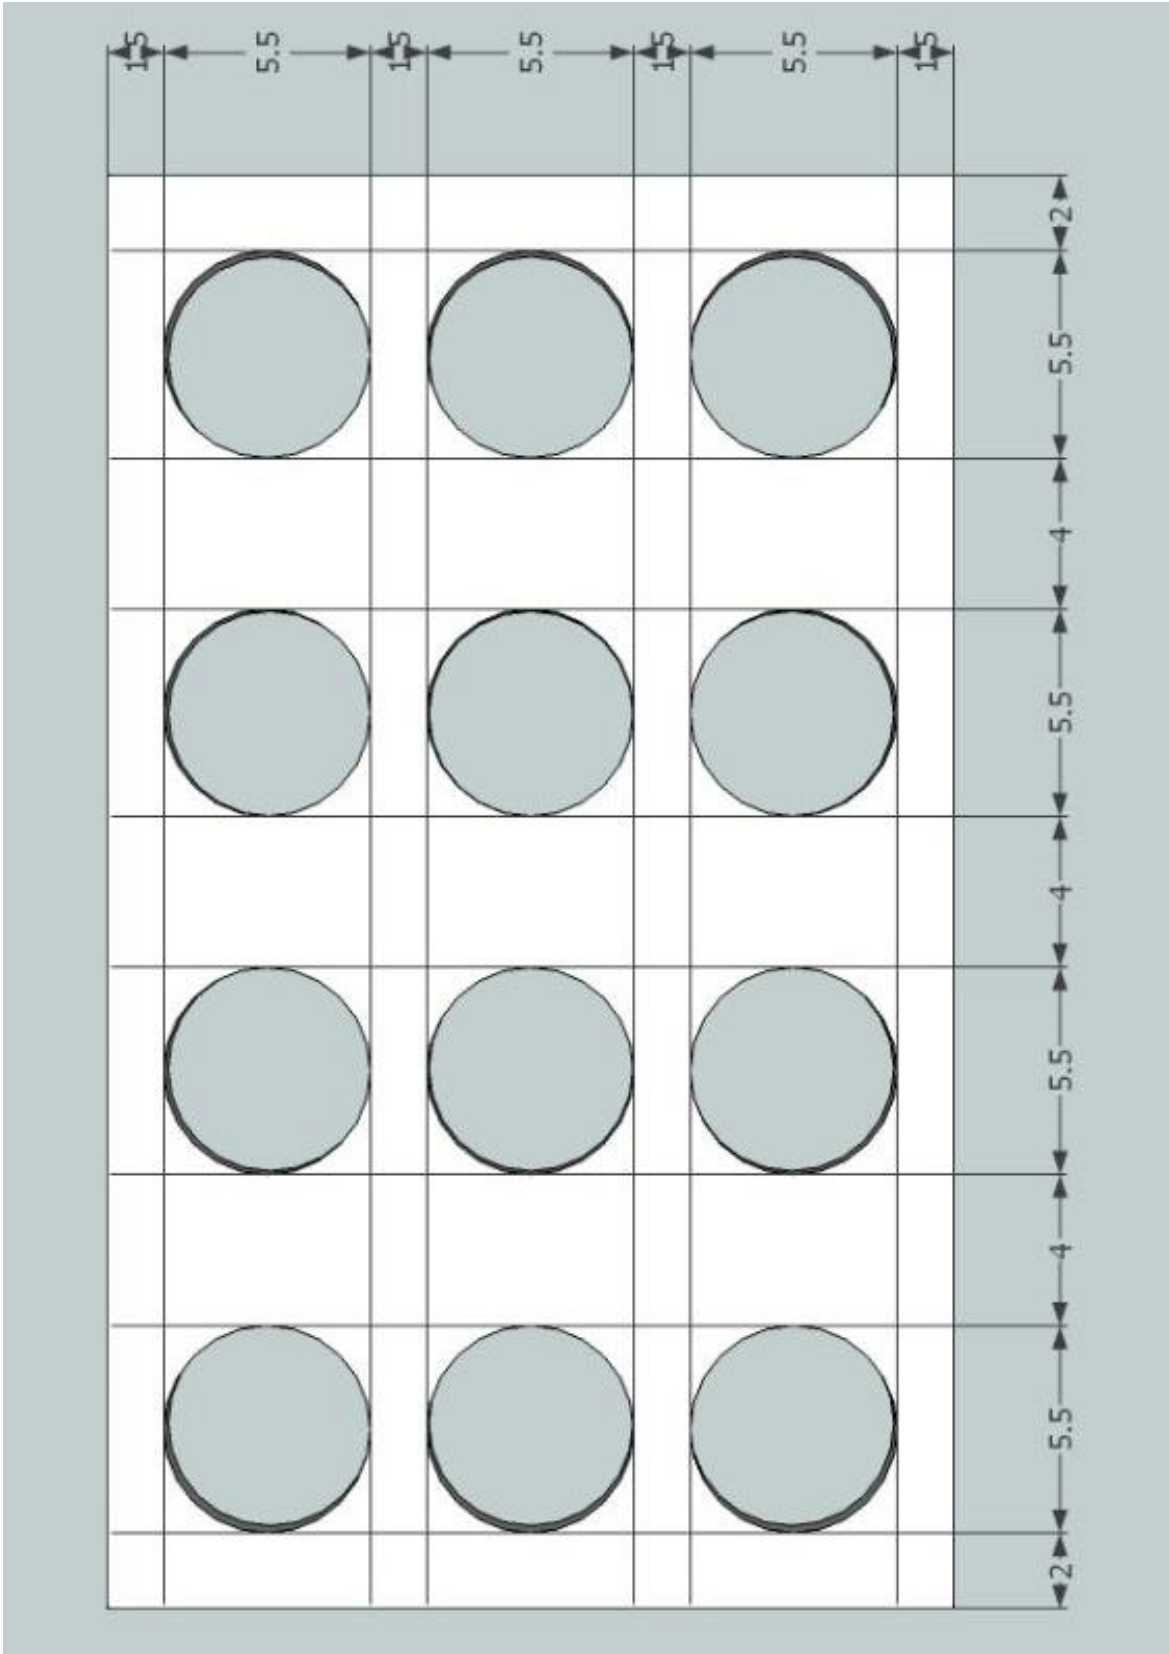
Vista superior de la gradilla, dimensiones en centímetros.
